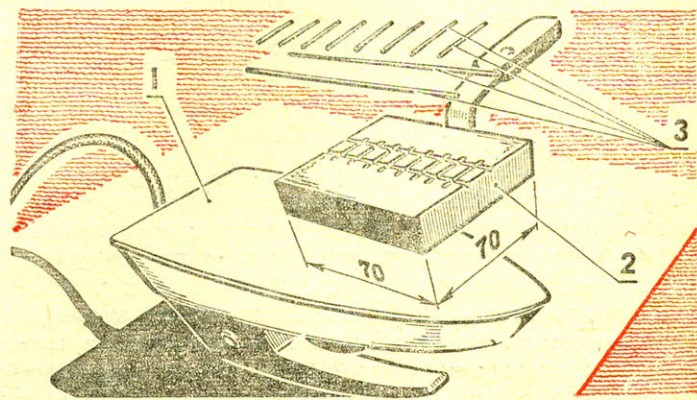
Устройство для пайки трапов: 1 — нагреватель (утюг), 2 — пластина-кондуктор, 3 — проволочные элементы трапа.
